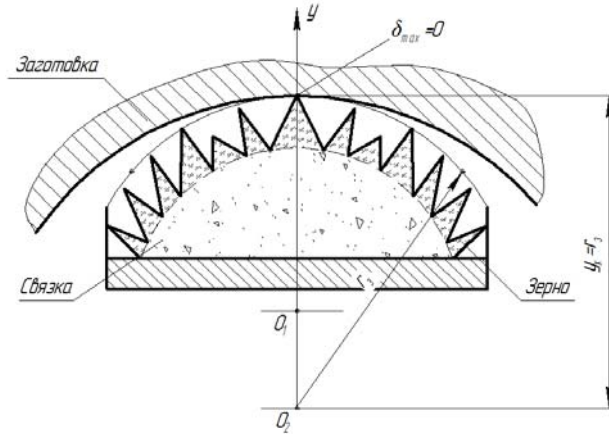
Схема касания алмазных зерен бруска с поверхностью заготовки
